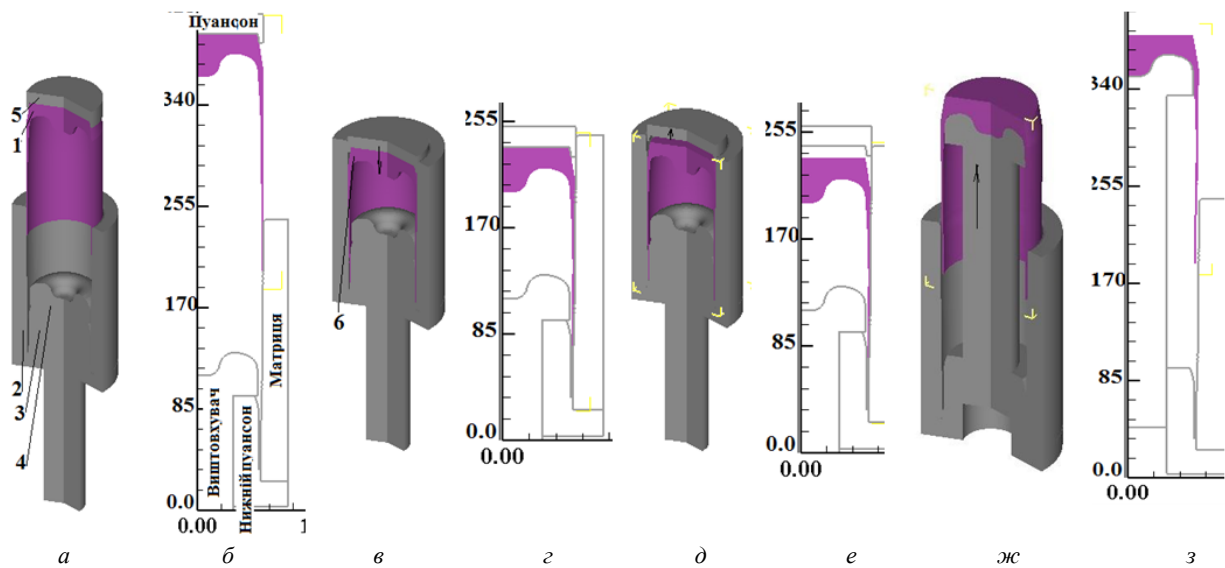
Розрахункові схеми в розрізі та розміри вихідної і zdeформованих заготовок з інструментом
